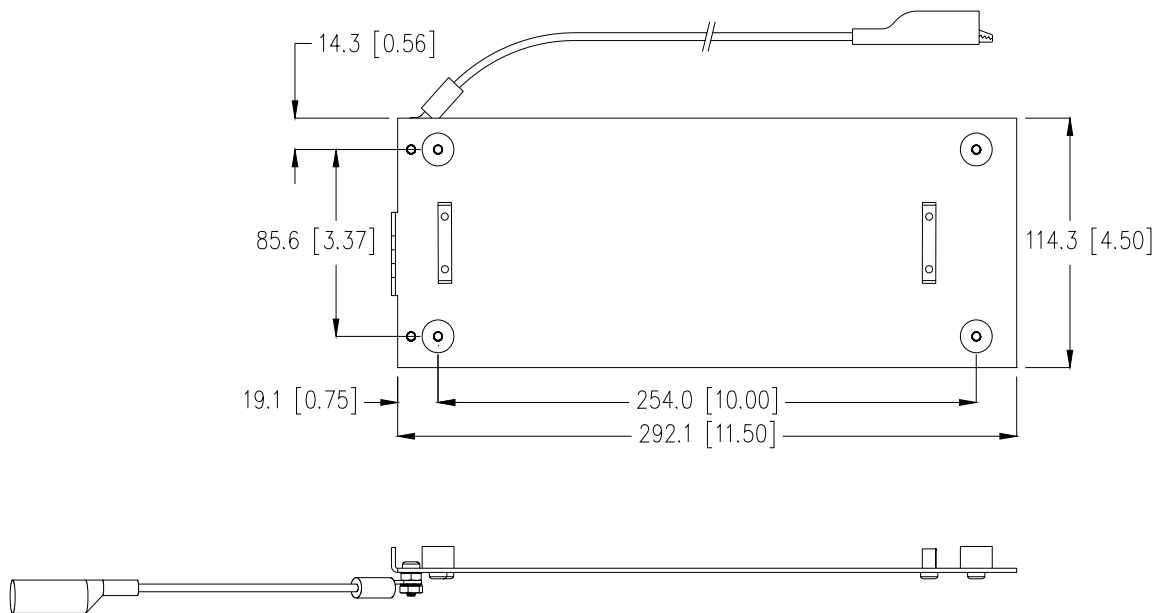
Приспособление для проверки датчиков воздушного зазора, кат. № 168448-01
